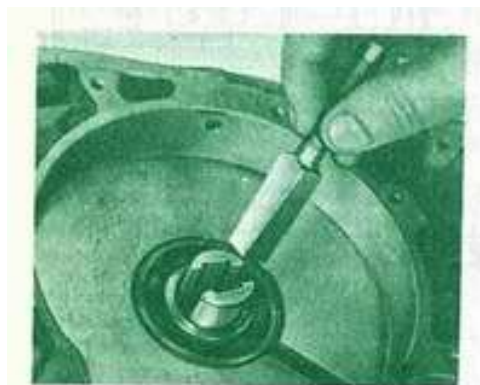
Приспособление для выемки внутреннего подшипника из левой половины картера
